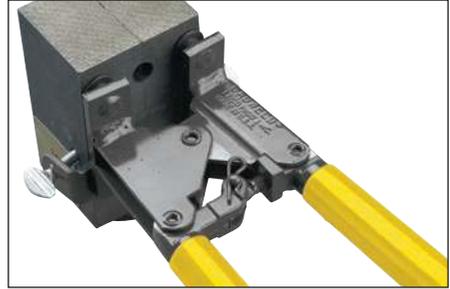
Fermer les poignées pour verrouiller fermement le moule. Vérifier que le moule est muni du joint approprié.
